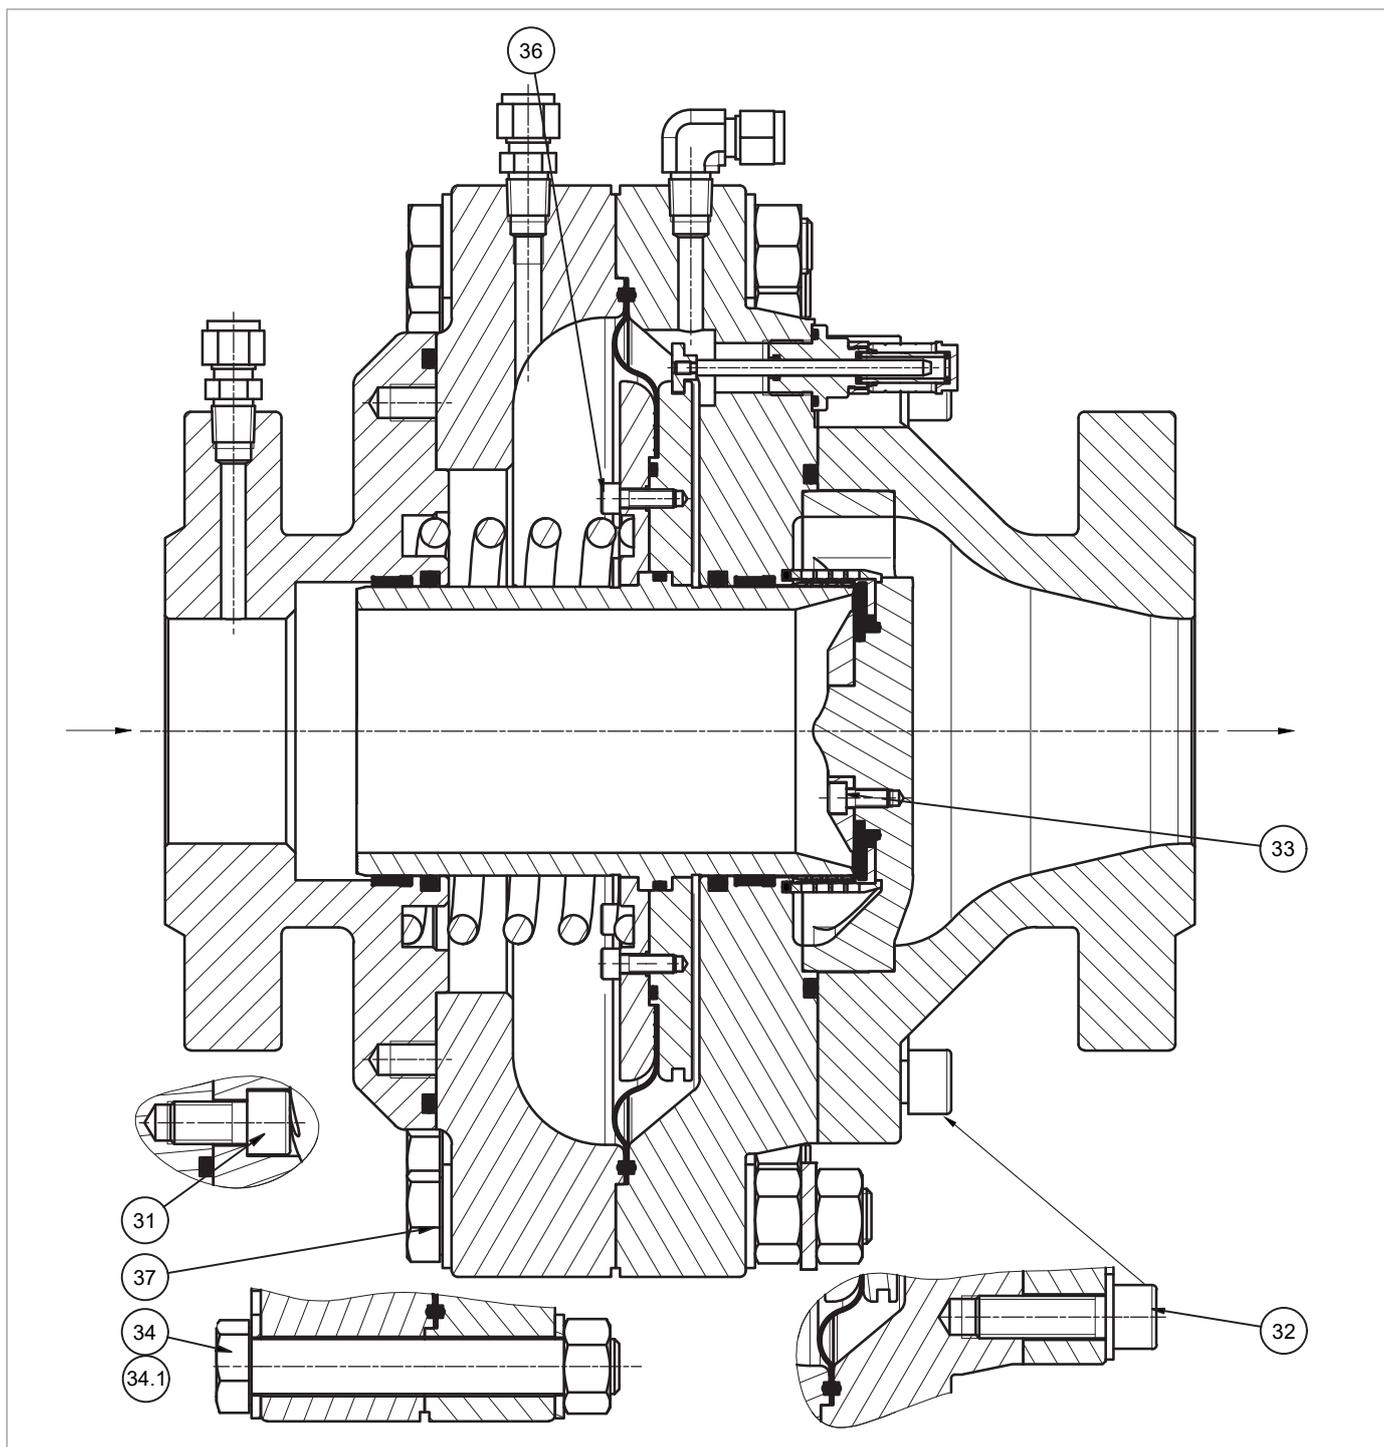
Моменты затяжки ASX 176 + Глушитель LDB/176
